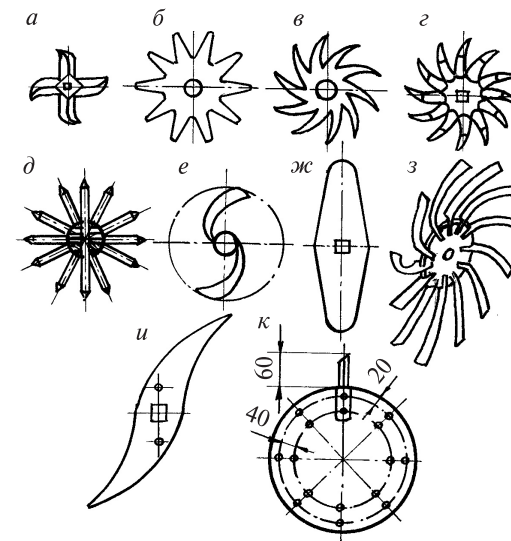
Конструкции рабочих органов ротационных борон: а – ножевые бороны; б, в – рыхлители; г – игольчатый диск; д – зубовой ротор; е – рабочий орган с криволинейной кромкой; ж – двухлопастный нож; з – рыхлительный диск; и – ножевидный рабочий орган; к – рабочий орган конической бороны
